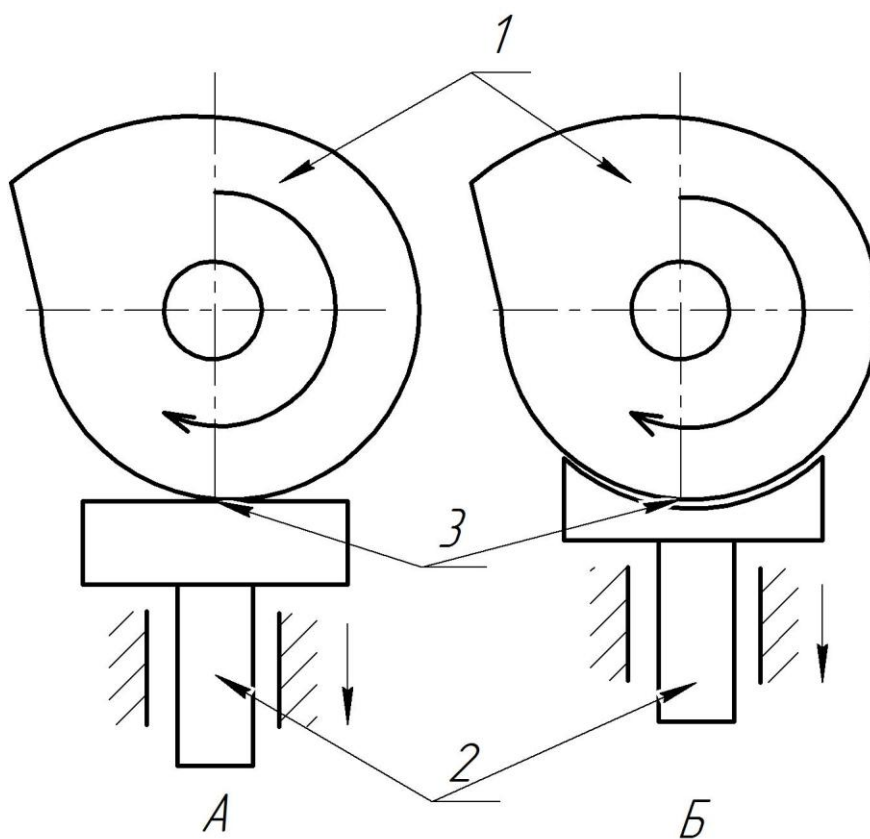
Схема кулачкового механизма, 1- профиль кулачка, 2 – толкатель, 3 – точка контакта.
